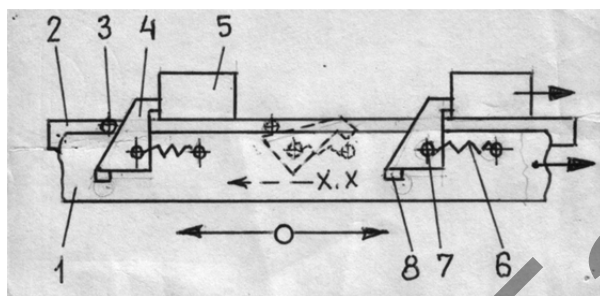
Схема модернизированной конструкции шагового конвейера
